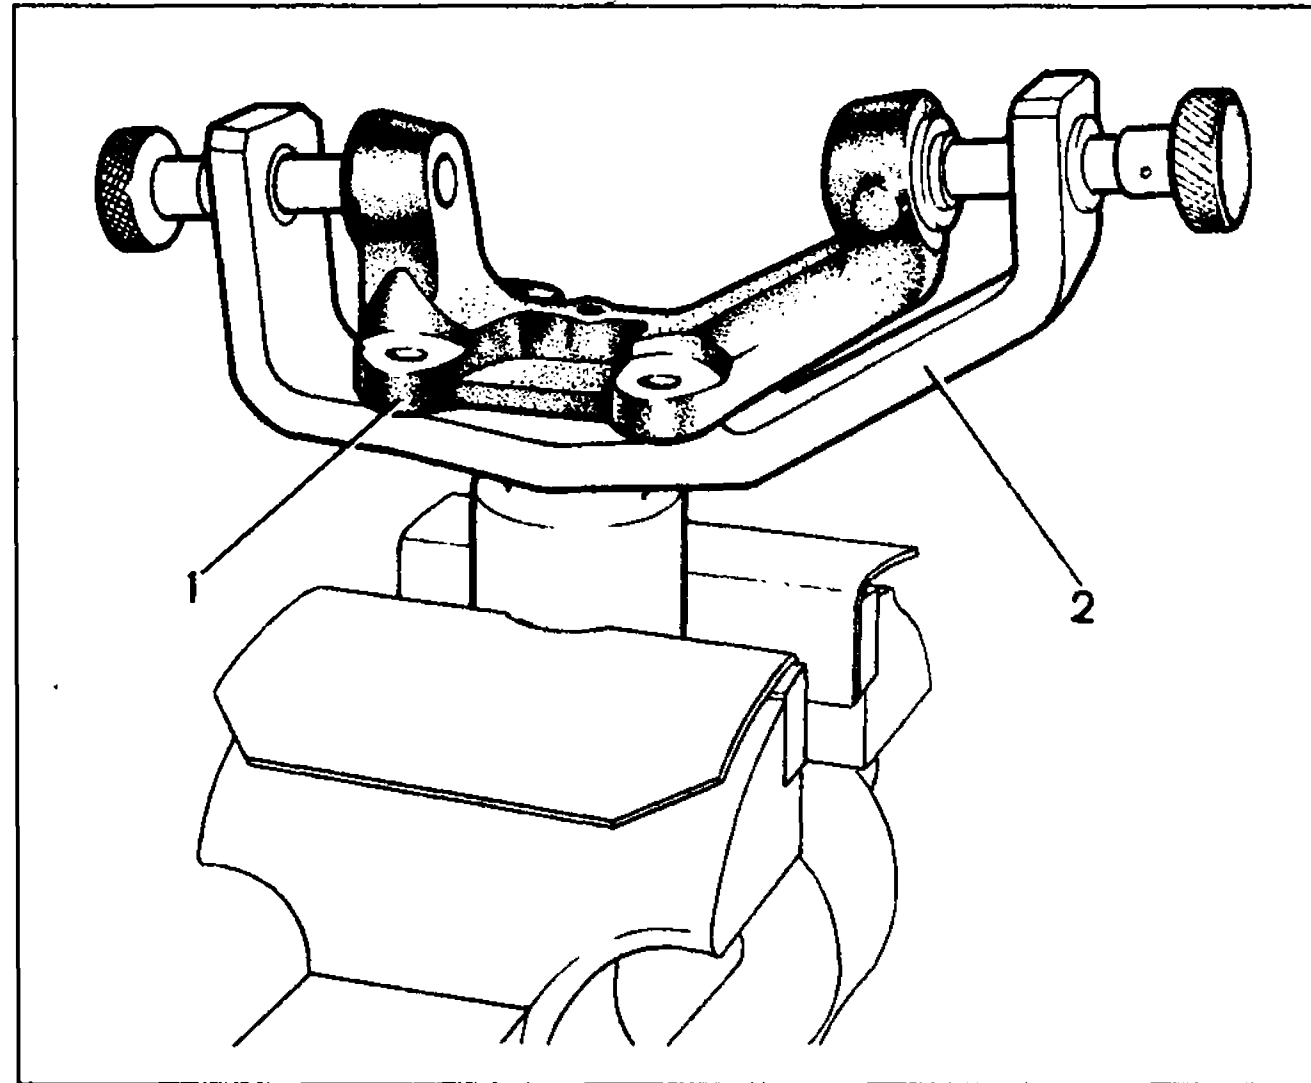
Выпрессовка шарниров нижнего рычага:
